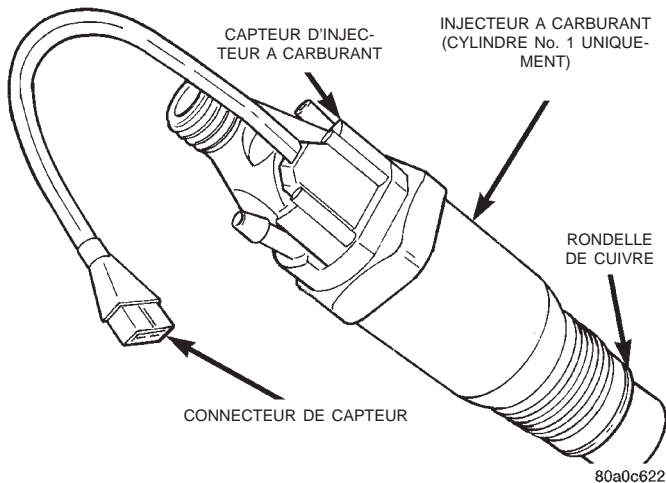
Capteur d'injecteur de carburant—cylindre No. 1
